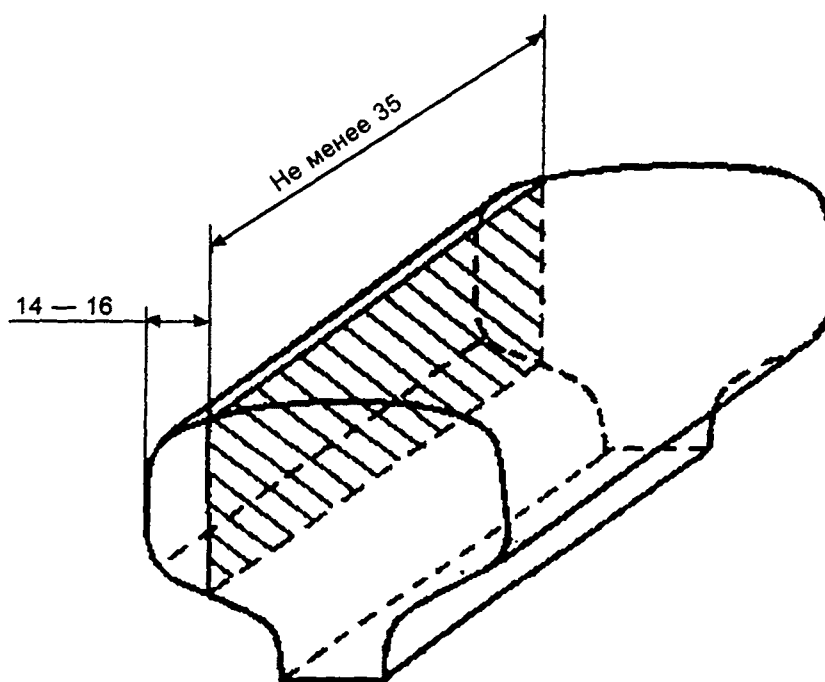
Схема вырезки микрошлифа и его размеры
